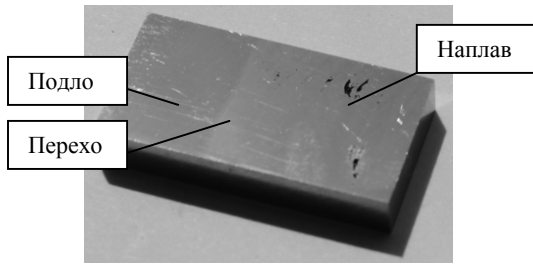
Поперечный макрошлиф образца для проведения коррозионных испытаний / Fig. 3. Transverse macrosection of the sample for corrosion testing
